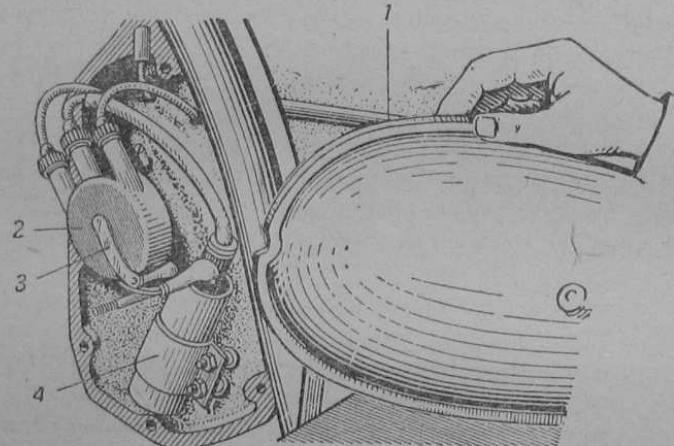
Установка прерывателя-распределителя и катушки зажигания:
